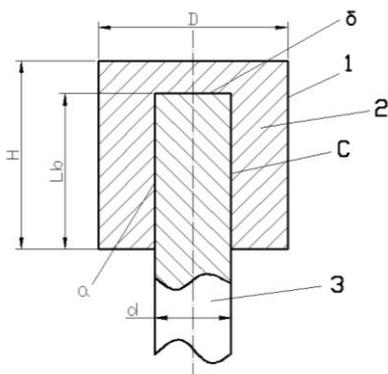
Сборная неразъемная заготовка (1), состоящая из элементарных заготовок: головной (2) и стержневой (3)
